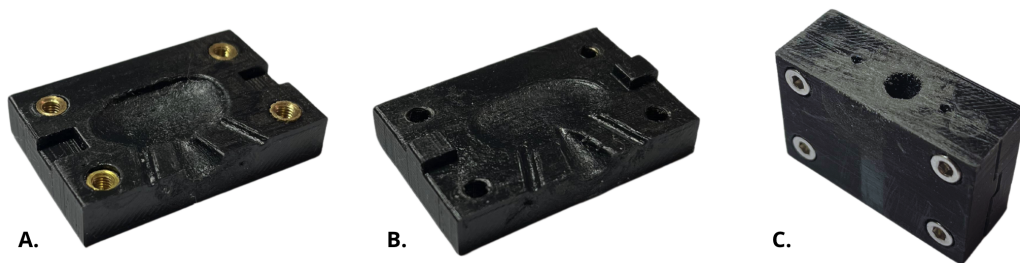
Molde para fabricar la parte anterior del prototipo de prótesis con resina acrílica dental, (A) vista isométrica de la sección superior, (B) vista isométrica de la sección inferior, (C) vista isométrica del molde ensamblado
